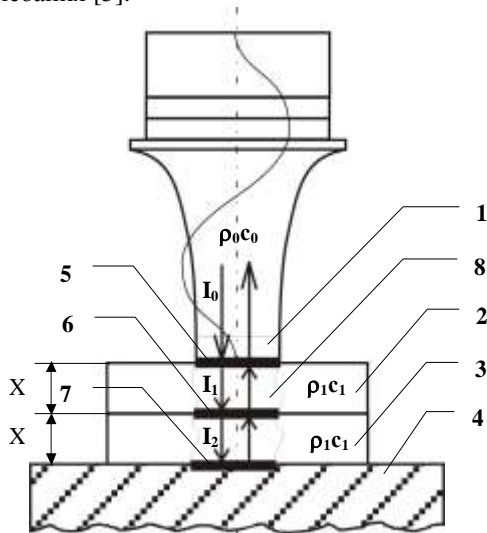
Схема процесса ультразвуковой сварки термопластов
